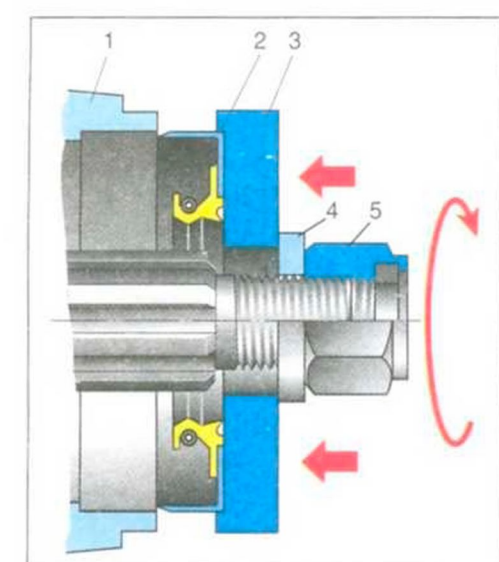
Запрессовка нового сальника: 1 — корпус; 2 — сальник; 3 — оправка; 4 — шайба; 5 — гайка
